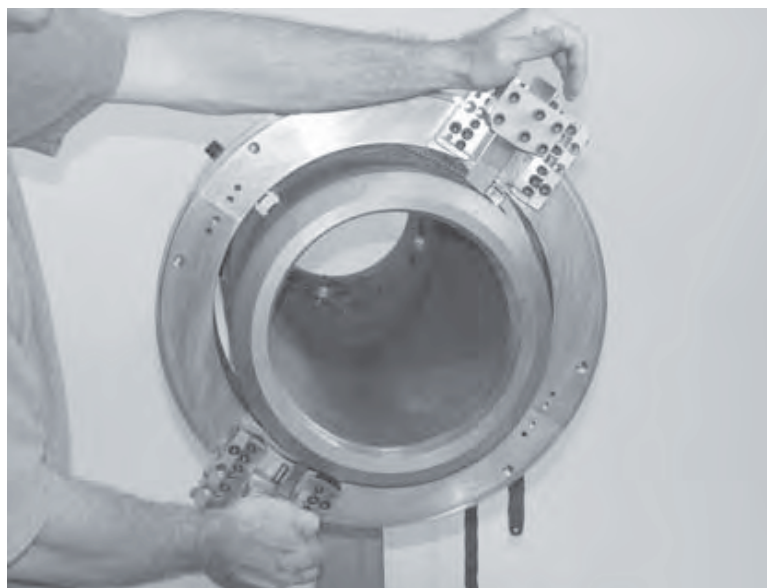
Проверните агрегат вручную для проверки зазора резца.
